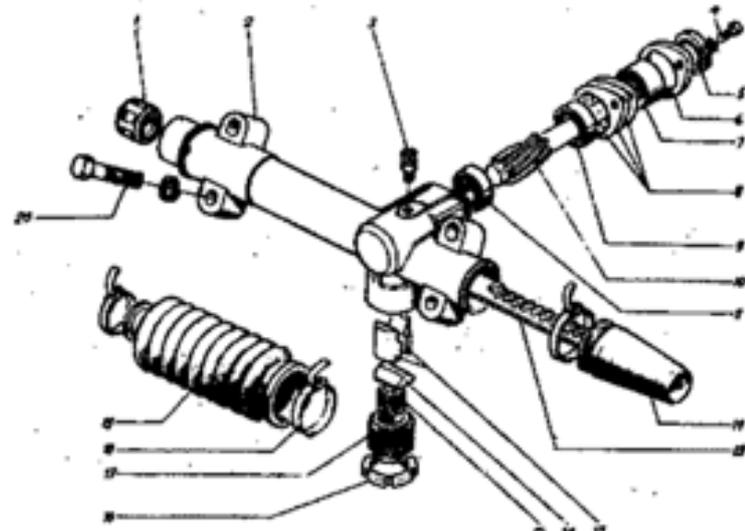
Детали рулевого механизма: 1 - втулка рейки; 2 - картер; 3 - сапун; 4 - болт крепления крышки; 5 - уплотнитель картера; 6 - крышка; 7 - втулка распорная; 8 - прокладка регулировочная; 9 - подшипник шестерни; 10 - шестерня рулевого механизма; 11 - чехол рейки левый; 12 - рейка; 13 - упор рейки; 14 - подпятник пружины; 15 - пружина; 16 - гайка стопорная; 17 - пробка картера; 18 - хомут; 19 - чехол рейки правый; 20 - болт крепления картера.
